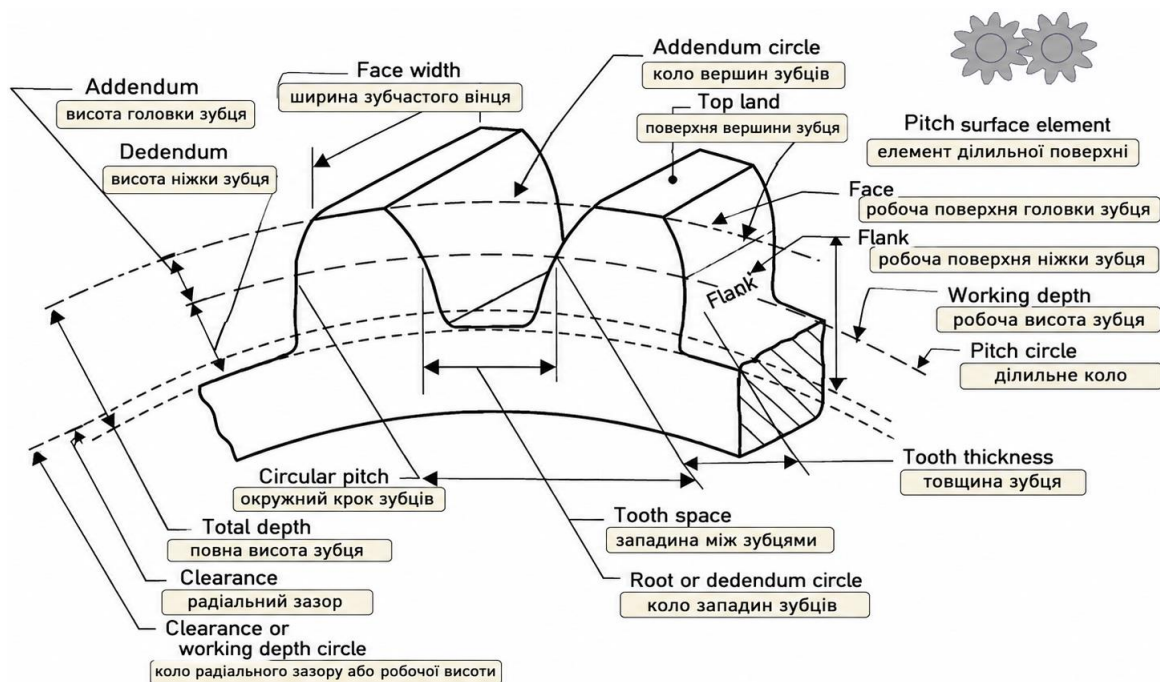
Основні геометричні елементи циліндричного зубчастого колеса зовнішнього зачеплення
